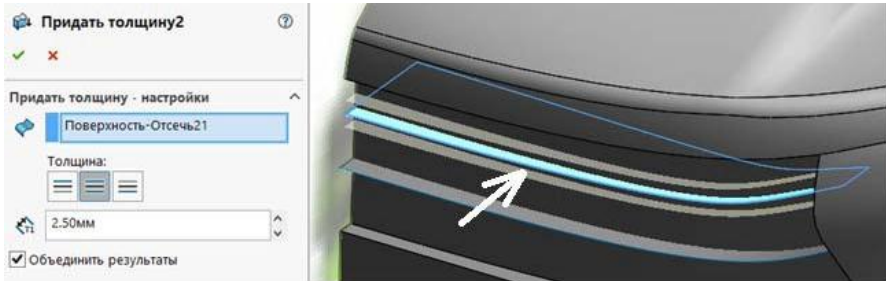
Процесс утворення твердотільного елемента з поверхні
